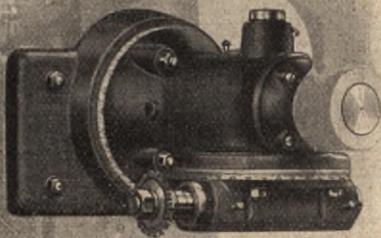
Universal-Fräskopf. Eingestellt zum Zahnstangen fräsen.
